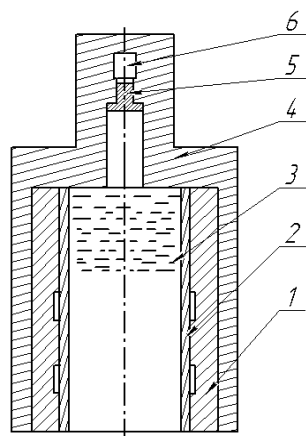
Навески порохового заряда в объеме рабочей передаточной среды над заготовкой, установленной в формообразующей полости инструмента: 1 - матрица, 2 – заготовка кольцевая, 3 – передающая среда (вода), 4 – матрицедержатель пресс-пушки, 5 – боек пресс-пушки, 6 – патрон (навеска пороха)
